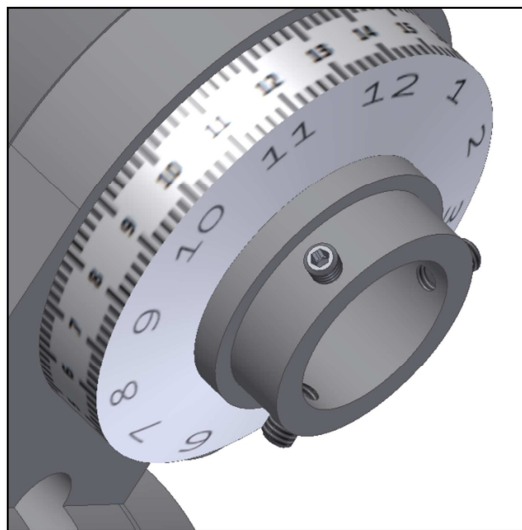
Lösen Sie die drei Sechskantschrauben.
